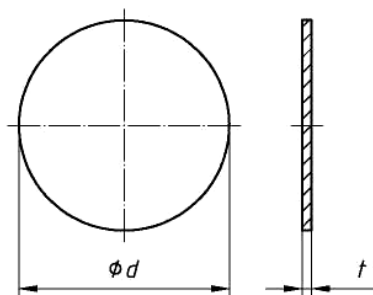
Размеры стекол для бортовых иллюминаторов
